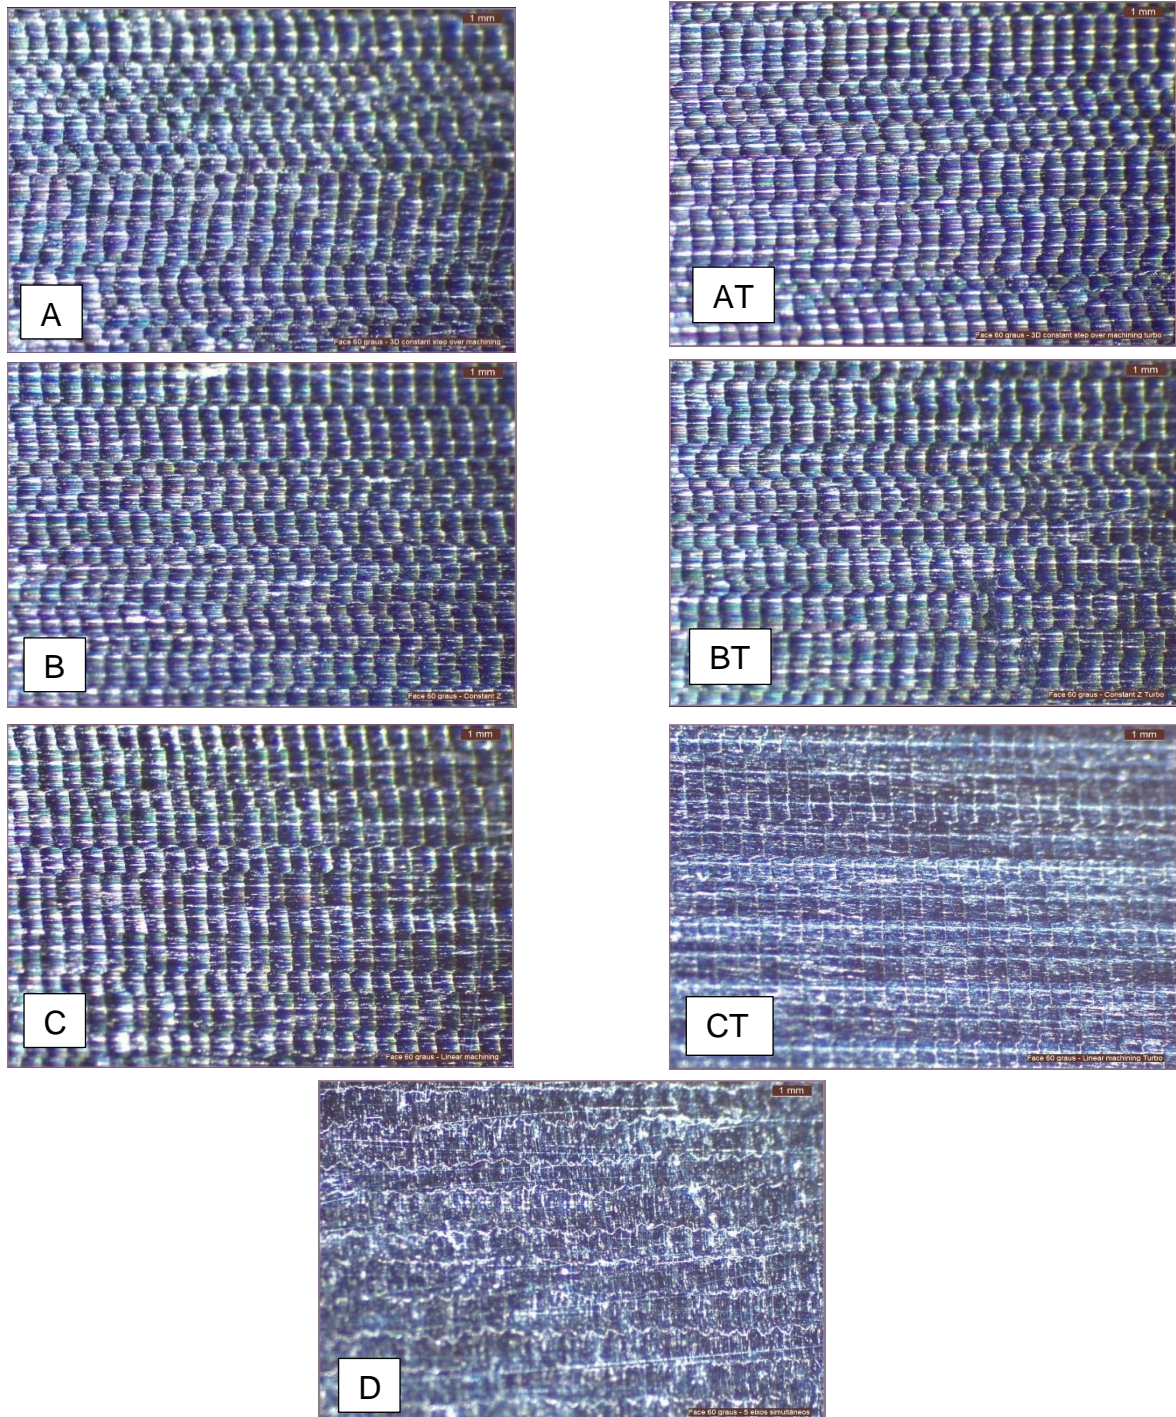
A: Estratégia de maquinagem Passagem constante 3D; AT: Estratégia de maquinagem Passagem constante Z 3D turbo; B: Estratégia de maquinagem Constante Z; BT: Estratégia de maquinagem Constante Z turbo; C: Estratégia de maquinagem linear; CT: Estratégia de maquinagem linear turbo; D: Estratégia de maquinagem 5 eixos simultâneos
